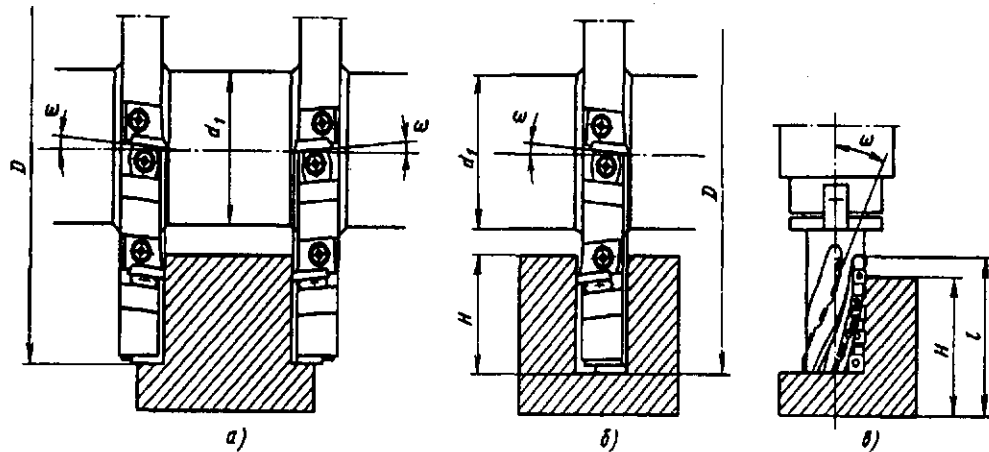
Схемы фрезерования: а — выступов набором двусторонних фрез; б — паза трехсторонней дисковой фрезой; в — уступа концевой фрезой
